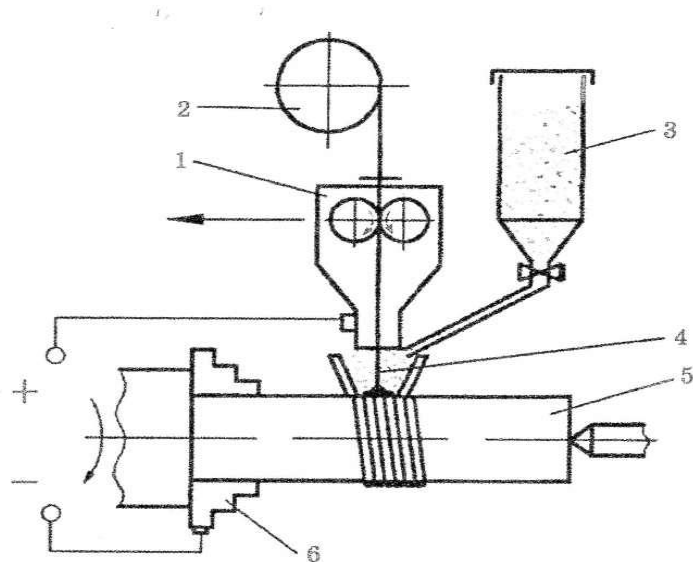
Принципова схема електродугового наплавлення деталей під флюсом: 1 – наплавлююча голівка; 2 – касета з електродним дротом; 3 – бункер з флюсом; 4 – електродний дріт; 5 – відновлювана деталь; 6 – патрон токарного верстату
